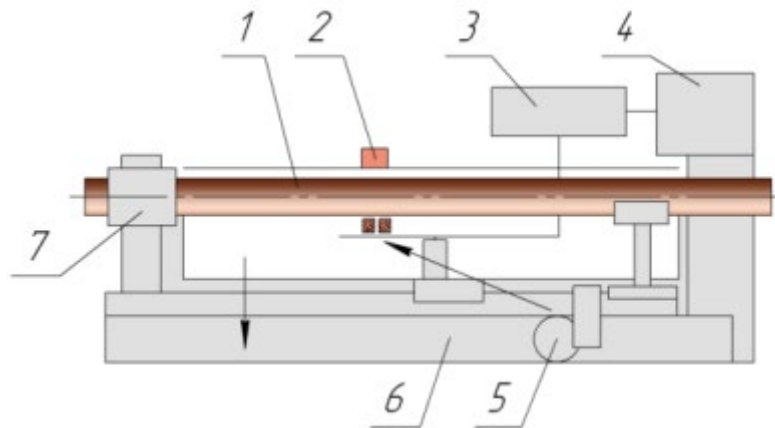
Схема установки для електролітно-плазмового зміцнювального оброблення циліндричних виробів типу колінчастий вал (бурова штанга):
